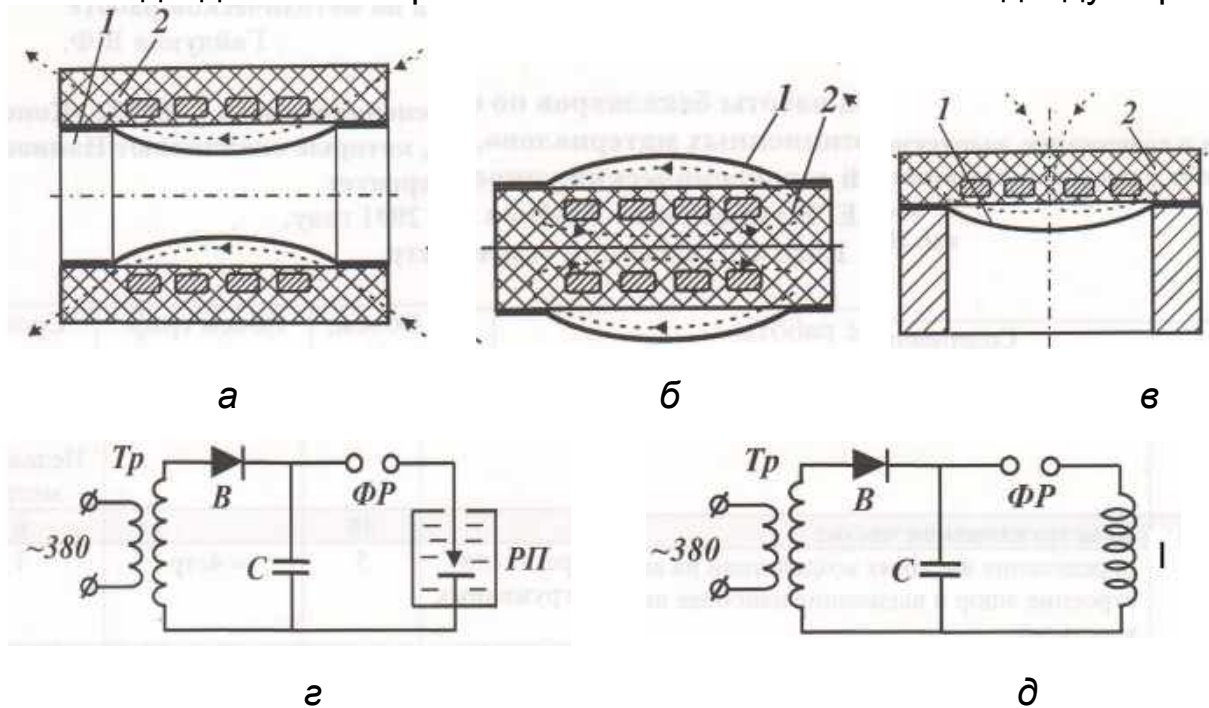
Принципові схеми магнітно-імпульсного штампування обтисканням трубної заготовки (а), роздачею трубної (б) і плоскої (в) заготовок: 1 – заготовка, 2 – індуктор (стрілками показано напрямки магнітних силових ліній); схеми генераторів імпульсних струмів для ЕГШ (д) і МІШ (е): Тр – високовольтний трансформатор, В – випрямляч, С – батарея, ФР – формувальний розрядник, РП – робочий проміжок, І – індуктор
